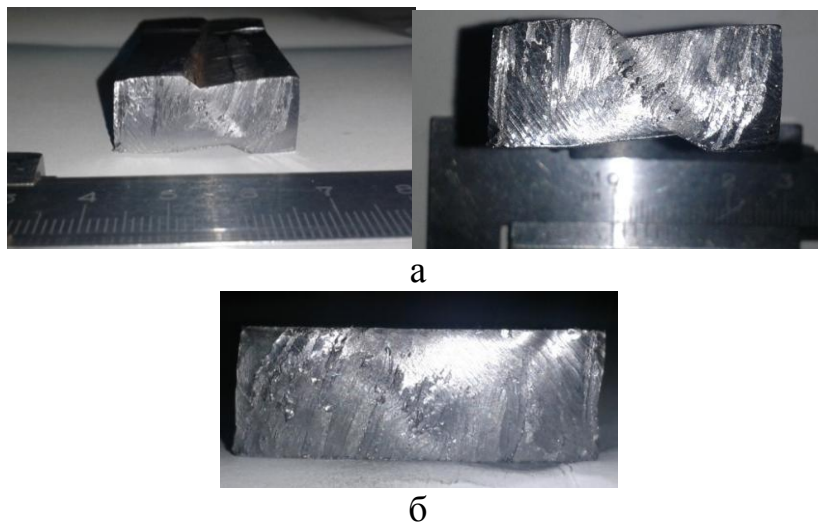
Заготовка после профилирования ступенчатыми бойками: а – с углом скоса ступеньки 45° , б – правки плоскими бойками
